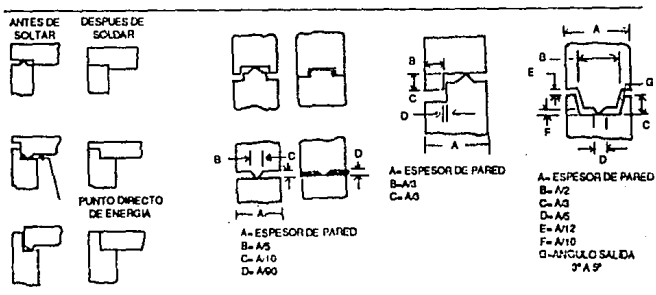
Recomendaciones para el diseño de la unión para soldadura ultrasónica. (Ref. 2).
